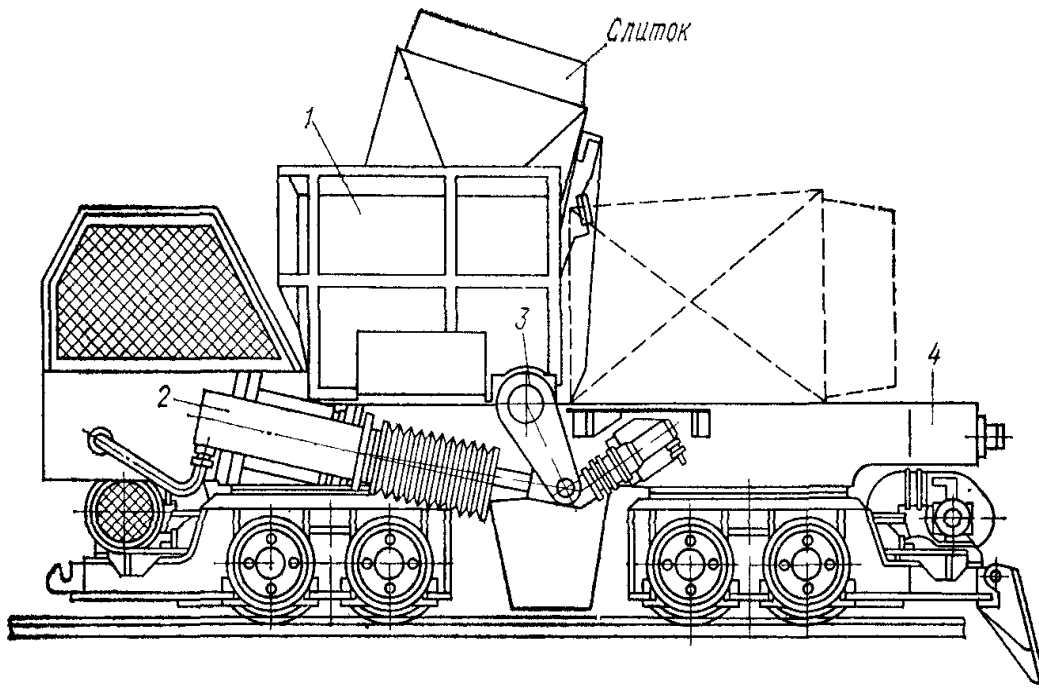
Загальний вигляд злитковозу слябінгу конструкції НКМЗ
